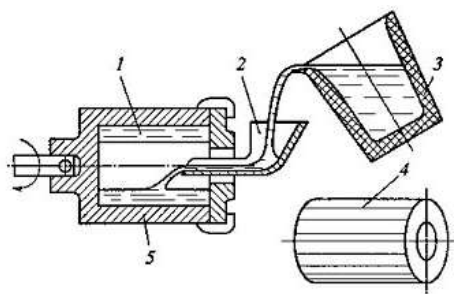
Відцентровий спосіб лиття. Схема отримання виливки при обертанні форми навколо горизонтальної осі: 1 – розплав; 2 – заливний жолоб; 3 – ківш; 4 – виливок; 5 – форма
